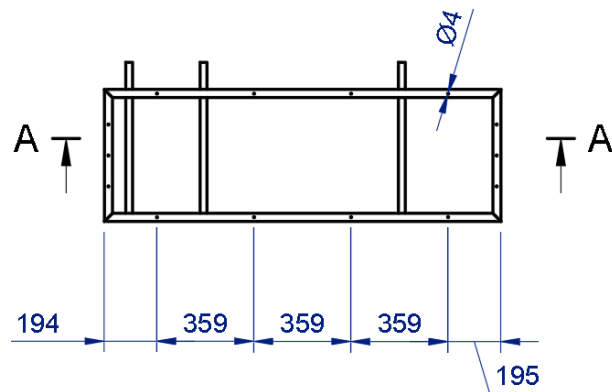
Desenho técnico da estrutura metálica. Fonte: Autora
